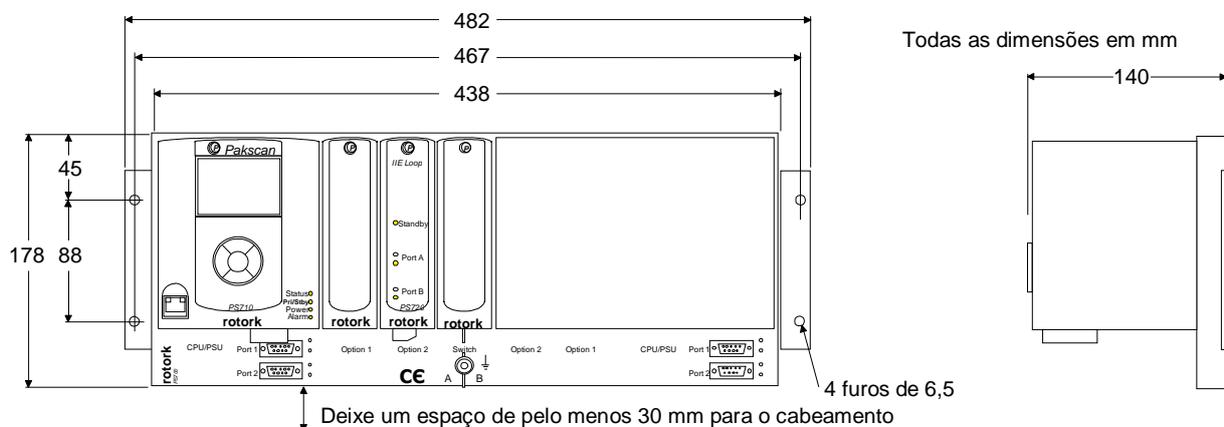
Dimensões de montagem em superfície do Pakscan 3.
